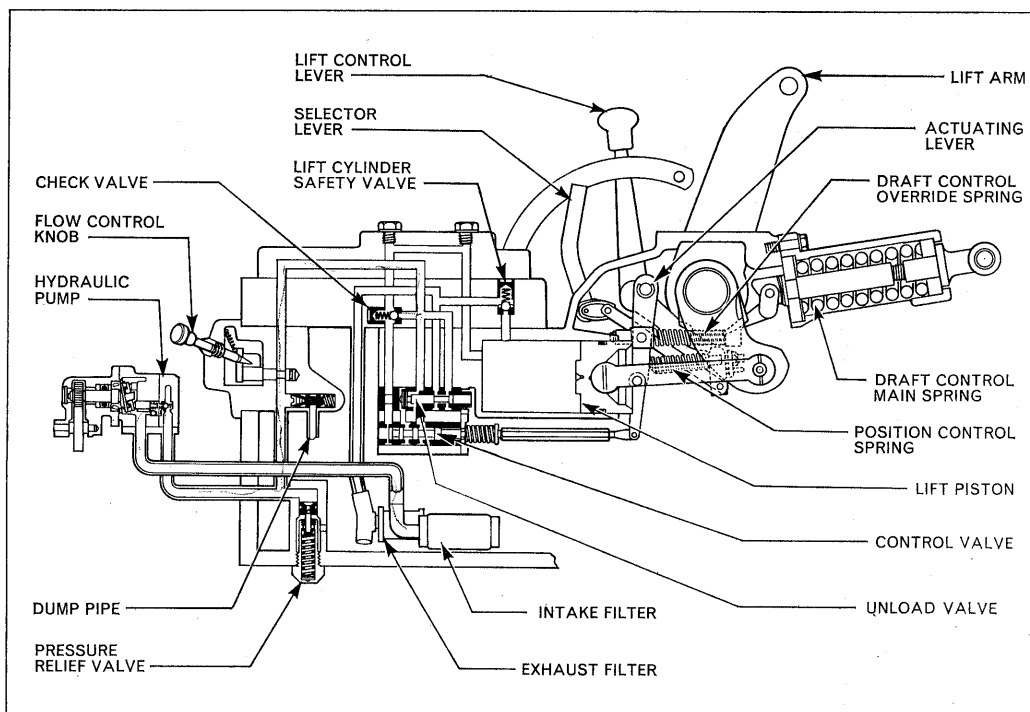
Principskitse for hydraulikanlægget - se tillige fig. 35 og 37.
